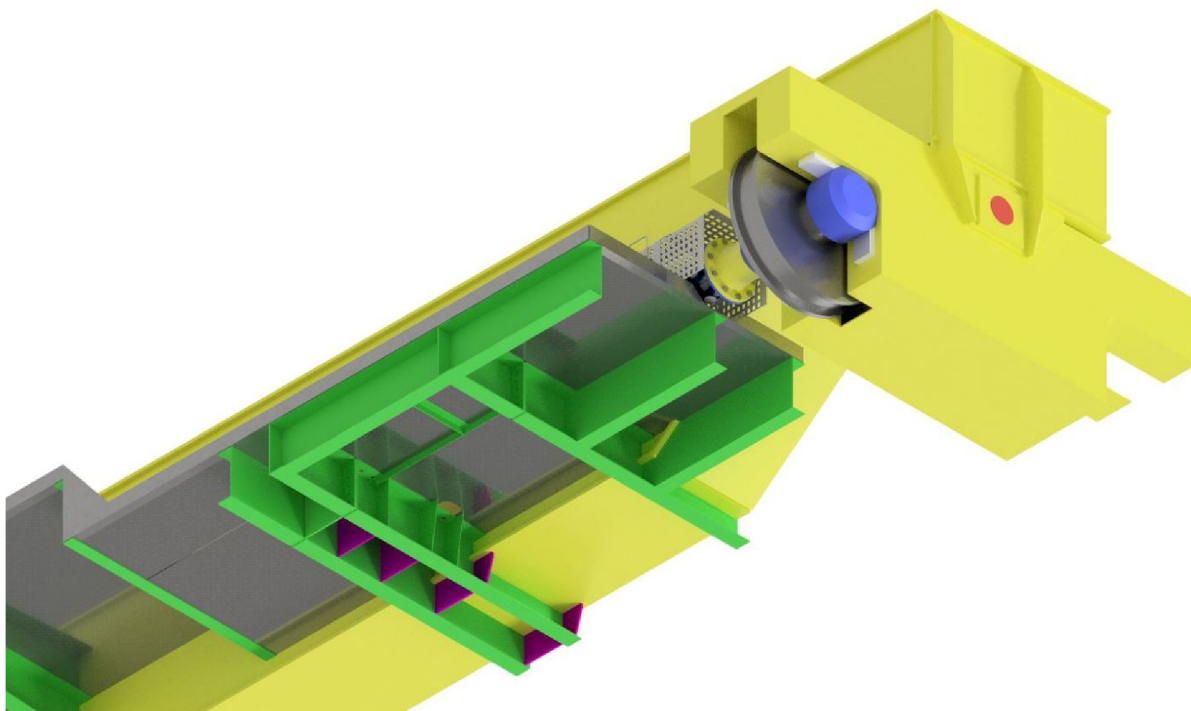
Mechanismy pojezdu – IZO pohled 1
